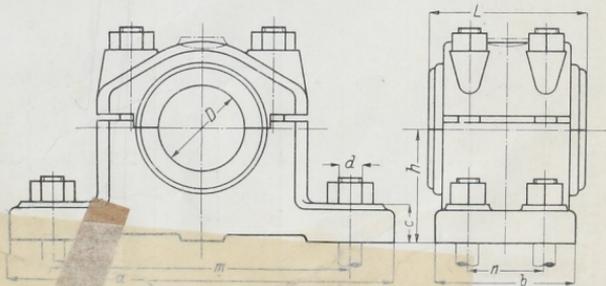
Deckellager mit vier Fußschrauben, nach DIN 506.
